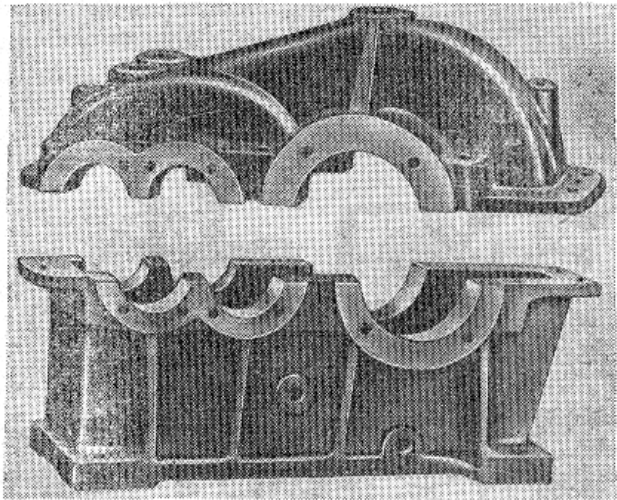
Литые корпус и крышка двухступенчатого цилиндрического редуктора с разъемом по осям валов
